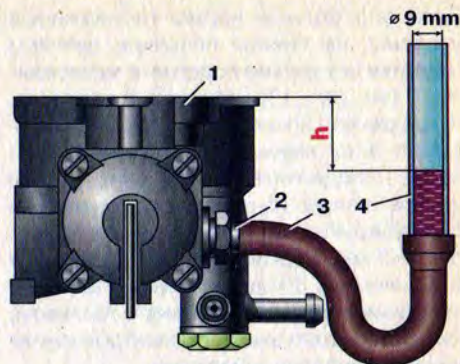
Схема проверки уровня топлива с помощью приспособления: 1 – корпус карбюратора; 2 – штуцер; 3 – гибкий шланг; 4 – прозрачная трубка; *h* – расстояние от уровня топлива до верхней плоскости разъема корпуса карбюратора
